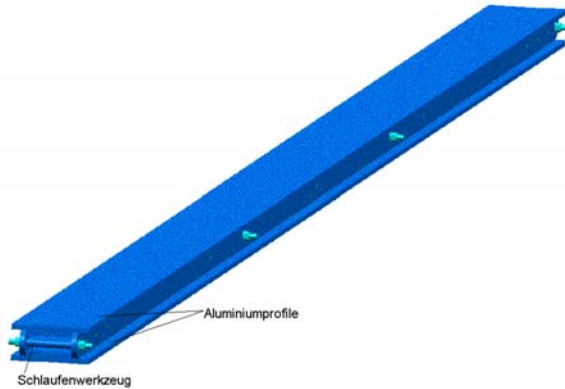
Schlaufenwerkzeug und Aluminiumprofile
